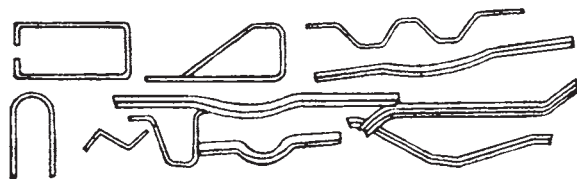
Типовые детали, изготавливаемые гибкой на горизонтальных гибочно-штамповочных прессах
